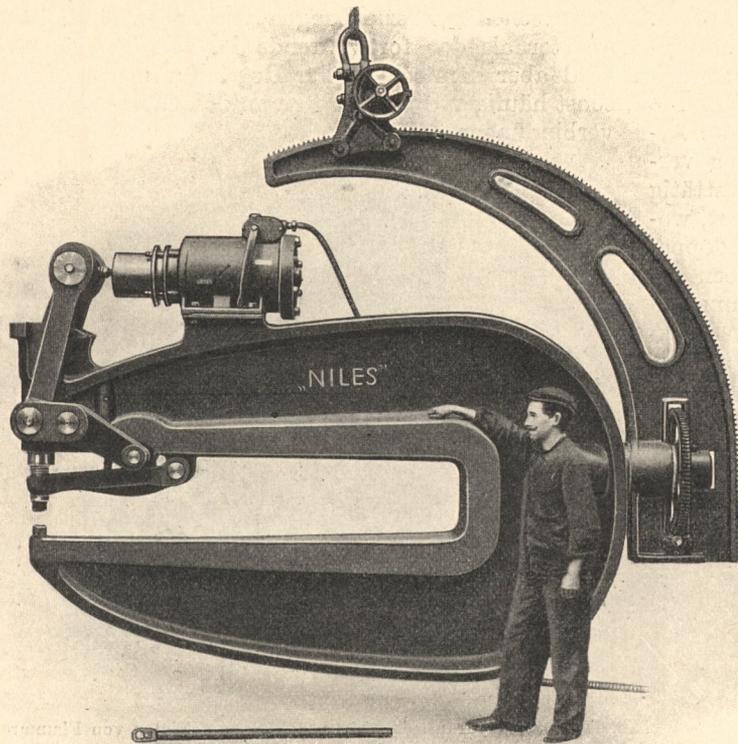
Bewegliche Preßluftnietmaschine mit Blechschlußvorrichtung. D. R. P. Ausführung: Deutsche Niles-Werkzeugmaschinenfabrik, Ober-Schöneweide-Berlin.
